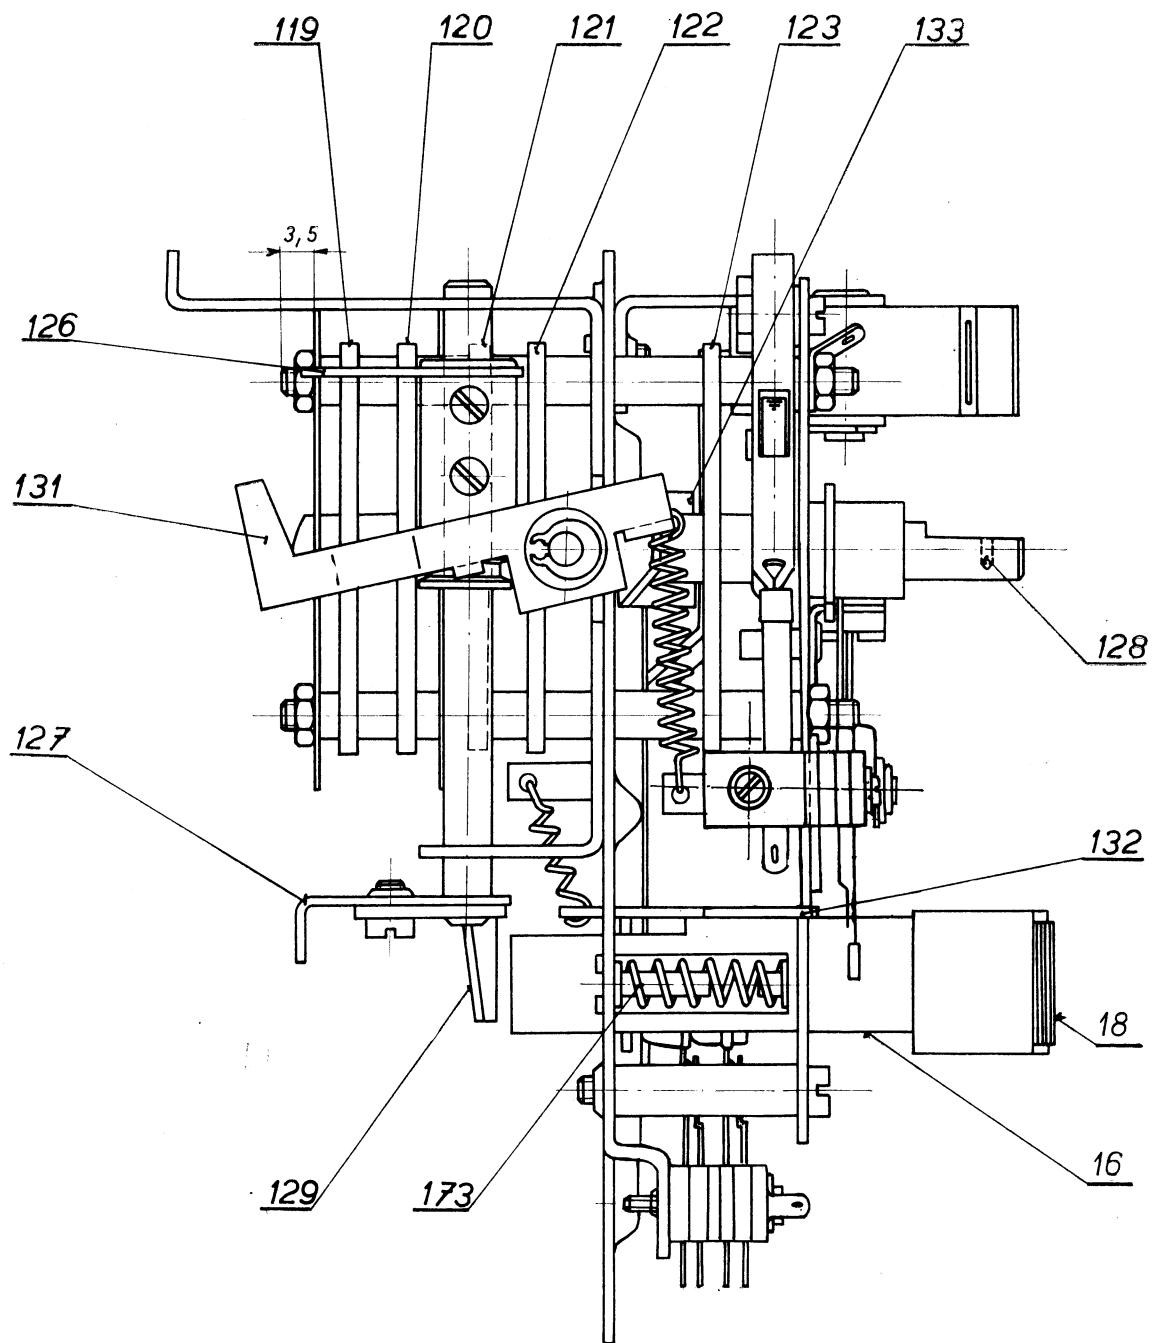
Náhradní díly — řez C—C (spojka)
